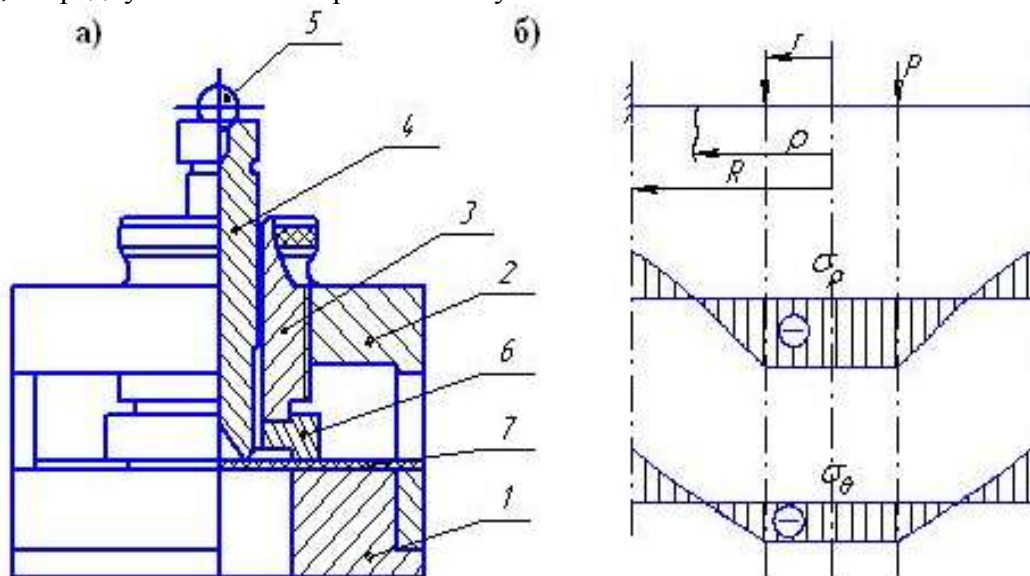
Приспособление для осесимметричного нагружения пластинки
